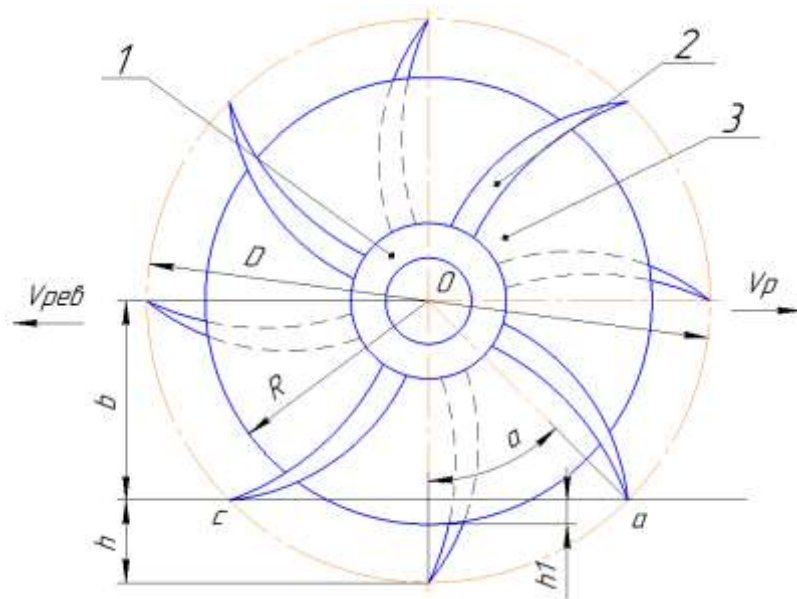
Розрахункова схема ротаційного зубового диска: 1 – ступиця; 2 – зуб; 3 – дисковий ніж;
